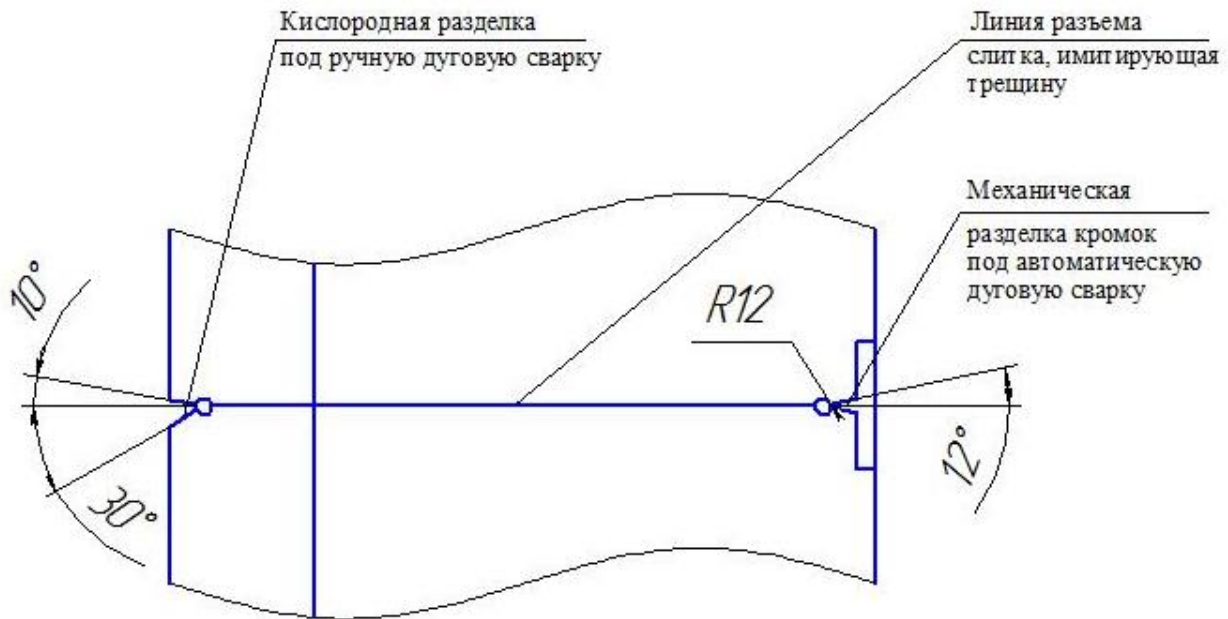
Схема разделки кромок под дуговую сварку
